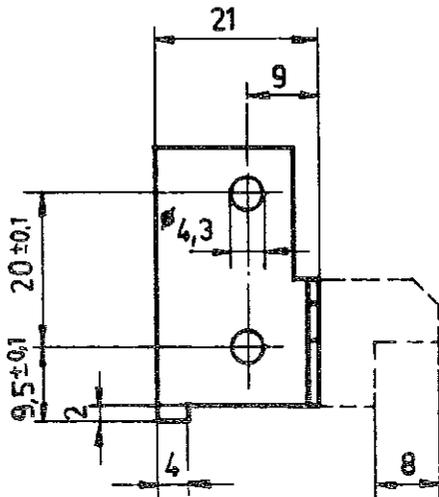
Durchbruch in der Gehäuserückwand bei Bedarf für einen Kabelsteckverbinder
